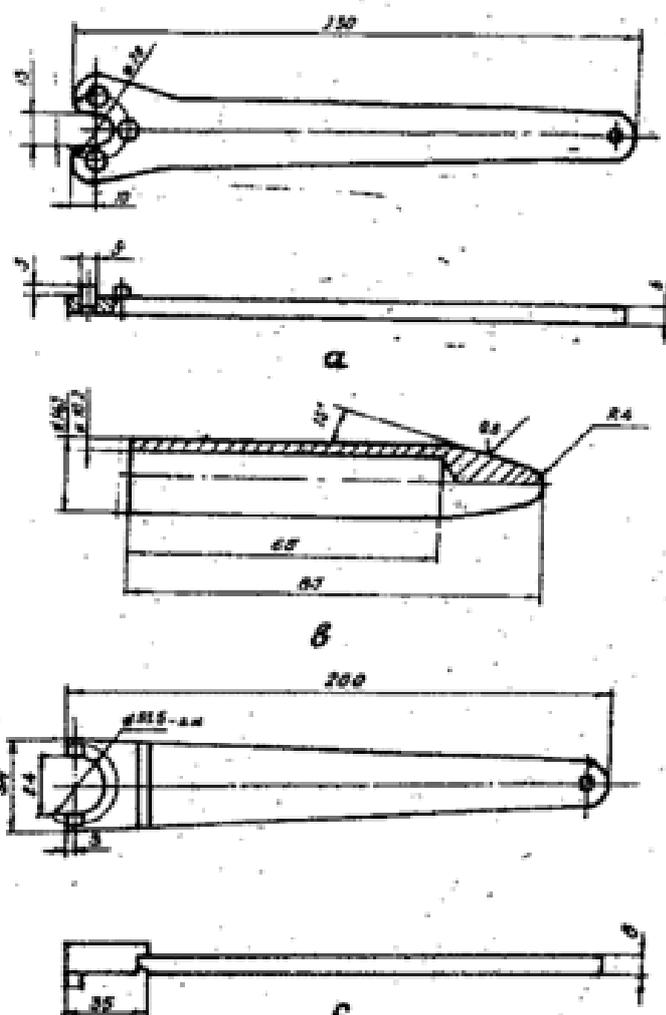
Инструмент и приспособление для амортизаторов передней и задней подвесок: а - ключ 9811-409 для гайки резервуара заднего амортизатора; б - оправка 9810-89 штока для надевания резиновой манжеты заднего амортизатора; в - ключ для гайки резервуара переднего амортизатора.
